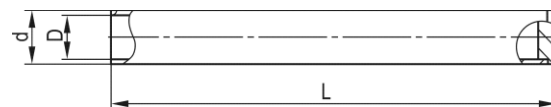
Гильза цилиндрическая сварная с монтажным кольцом OS3
